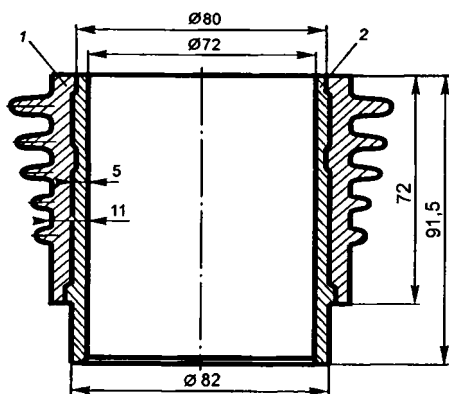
Биметаллический цилиндр пневмокомпрессора трактора «Беларус»:
